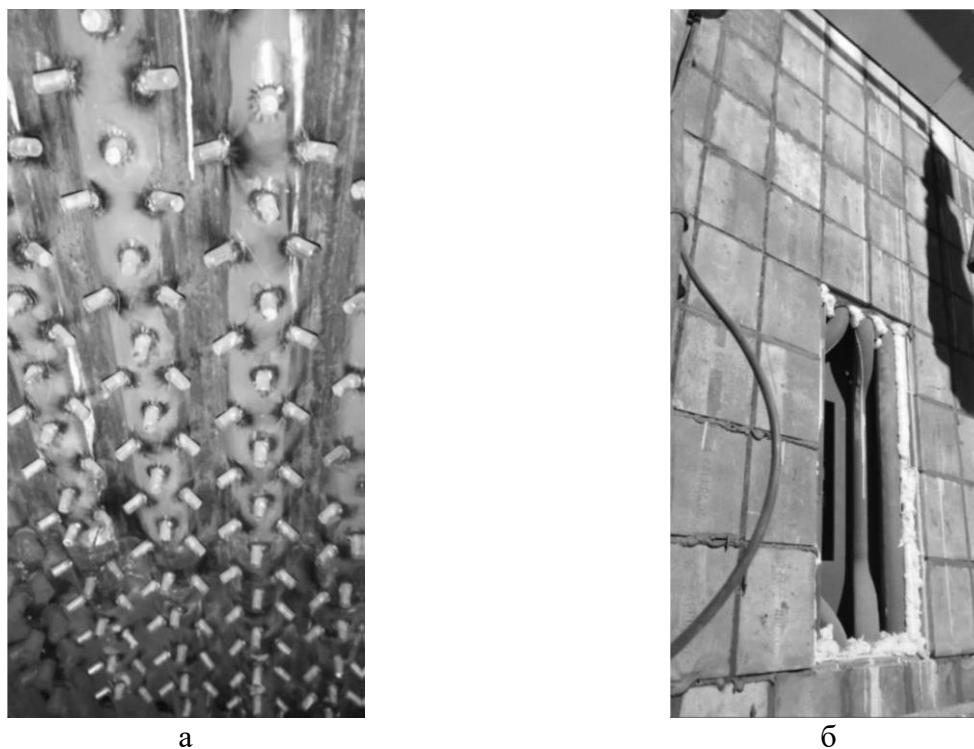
Конструкция футеровки первого газохода котла для сжигания ТКО:
